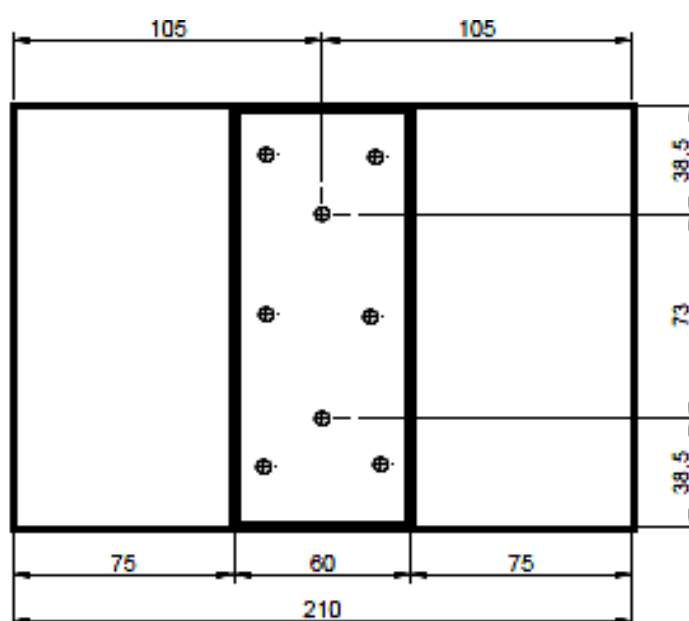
Esquema de montagem dos blanks patchwork, onde os círculos na figura indicam os pontos de solda com as medições em mm.
